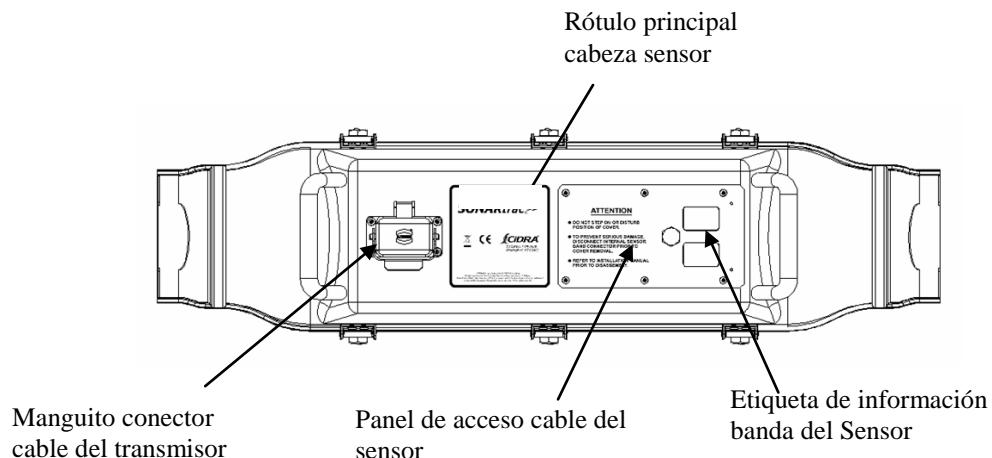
Vista Exterior del Ensamble de la Cubierta Superior del Sensor
